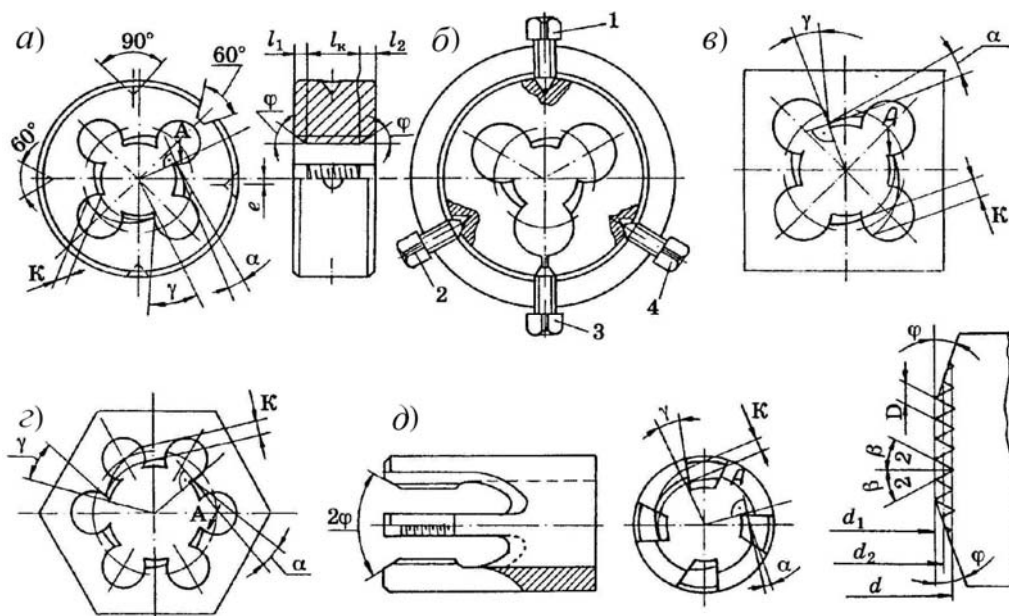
Резьбонарезные плашки (а, в, г, д) и их крепление в плашкодержателе (б)
